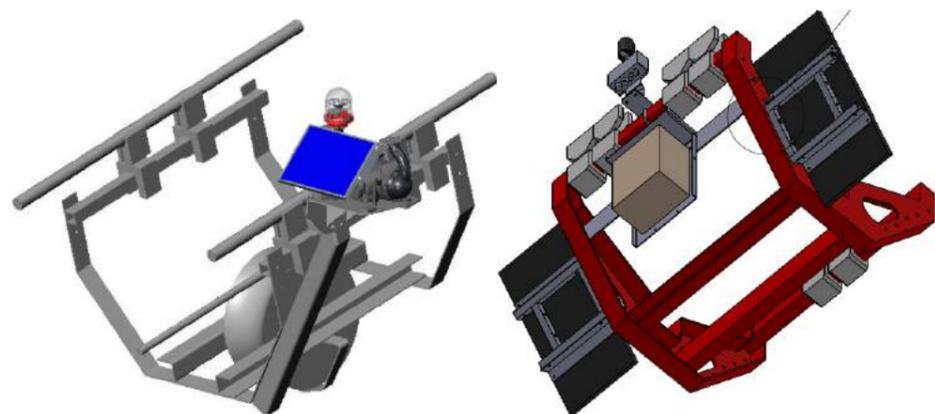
Exemples de cavaliers équipés de balisages aériens (Source : Groupement POMA)
